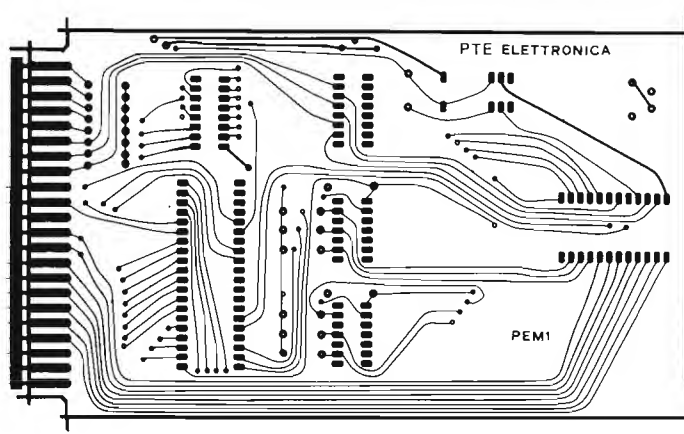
a-b - Disegno del circuito stampato. Sotto foto della scheda montata.
